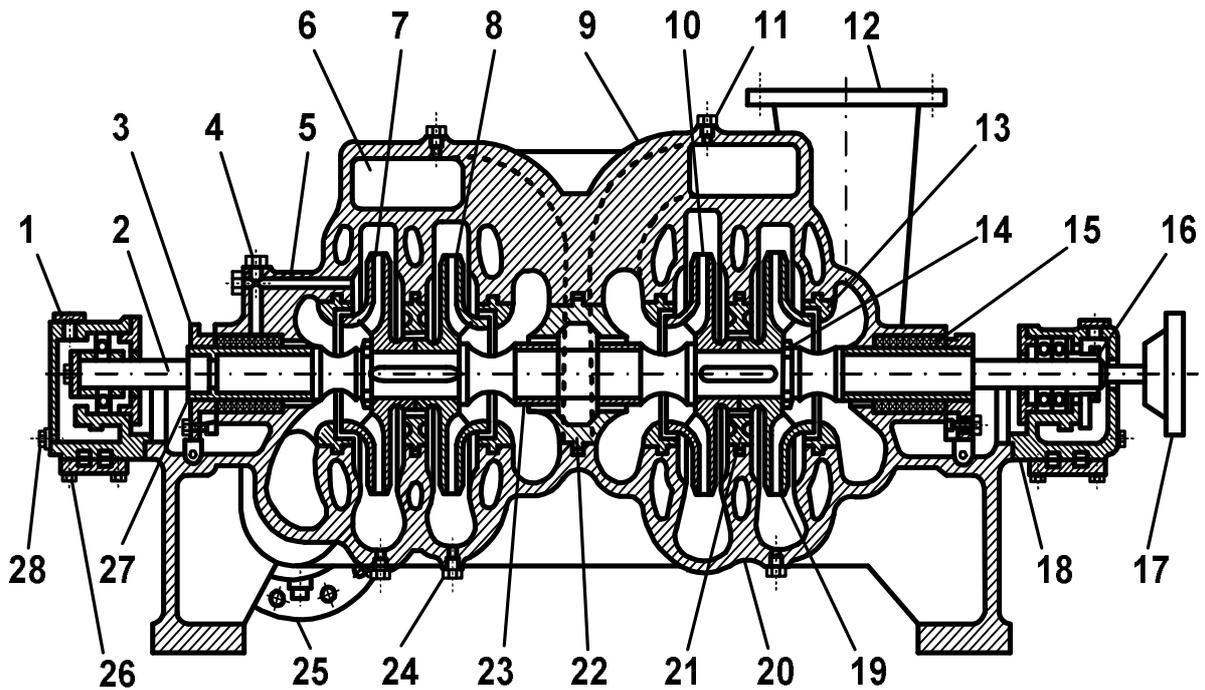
Насос ЦН400-210 (ЗВ-200×4): 1 и 18 – передняя и задняя подшипниковая опора; 2 – вал; 3 – фланец сальника; 4 и 5 – заглушка и канал подвода воды на гидрозатвор сальника; 6 – перепускной канал; 7 и 8 – рабочее колесо 1-й и 2-й ступени; 9 и 20 – верхняя и нижняя часть корпуса насоса; 10 и 19 – рабочее колесо 3-й и 4-й ступени; 11 и 24 – верхняя и нижняя пробки корпуса; 12 и 25 – напорный и всасывающий патрубки; 13 – кольцевые уплотняющие втулки; 17 – полумуфта; 21 и 22 – уплотняющие вкладыши; 23 – уплотняющие кольца; 26 – заглушка опоры; 27 – защитная втулка сальника; 28 – пробка для слива масла
